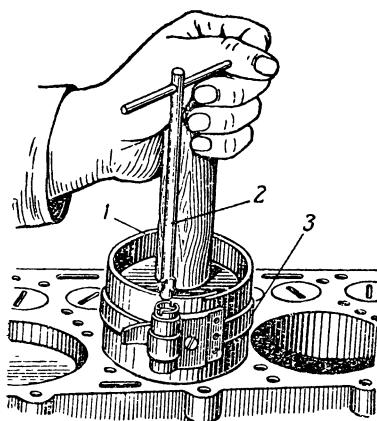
Установка собранного поршня в цилиндр двигателя:
